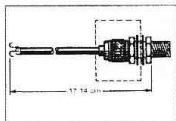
Détails d'assemblage du connecteur sur le capteur du balun.
